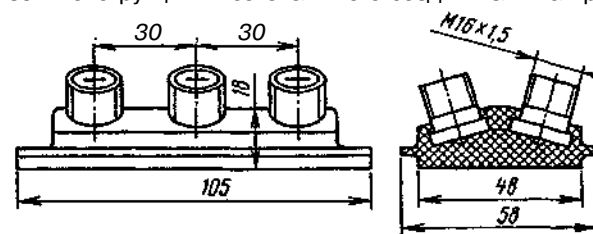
Конструкция высоковольтного соединителя на шесть гнезд
